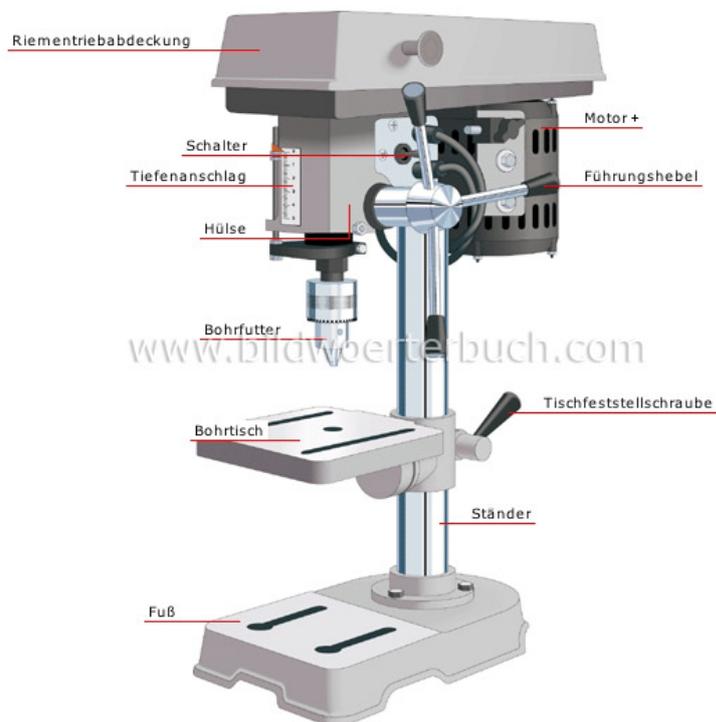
Aufbau einer Ständerbohrmaschine; Quelle: Internet
